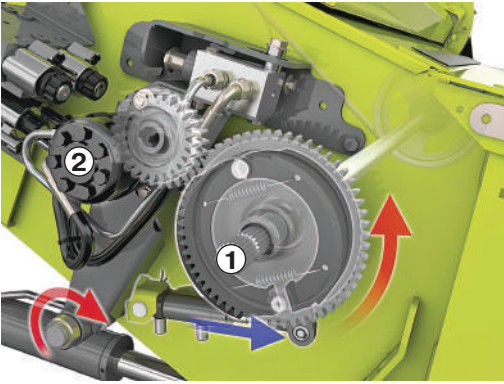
Гальмо приводу жатки та гідрореверс:
